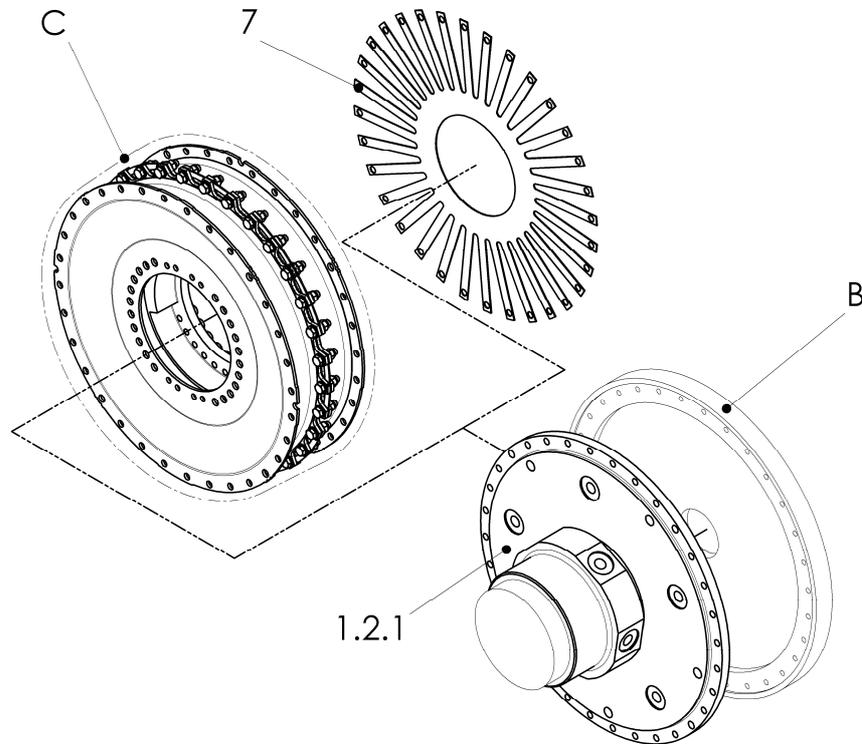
Baugruppe Gummielement und Lüftungsblech platzieren
